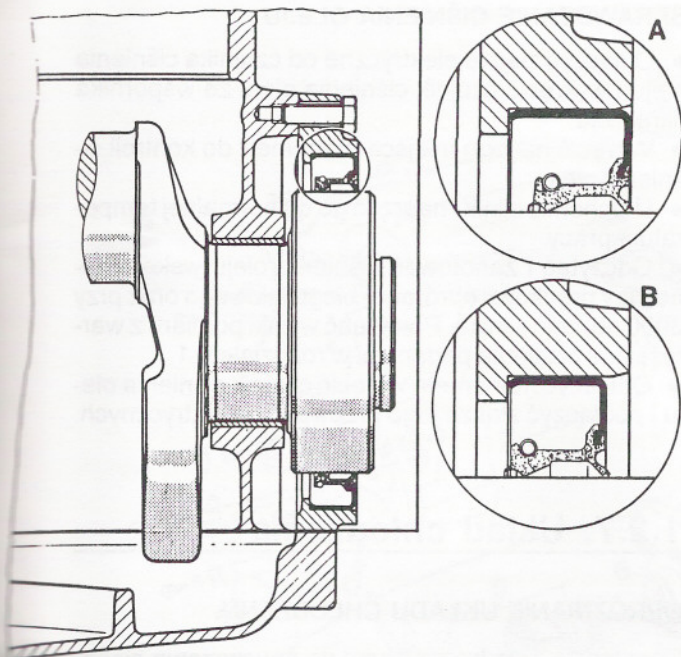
Przednie łożysko wałka sprzęgłowego skrzynki biegów
